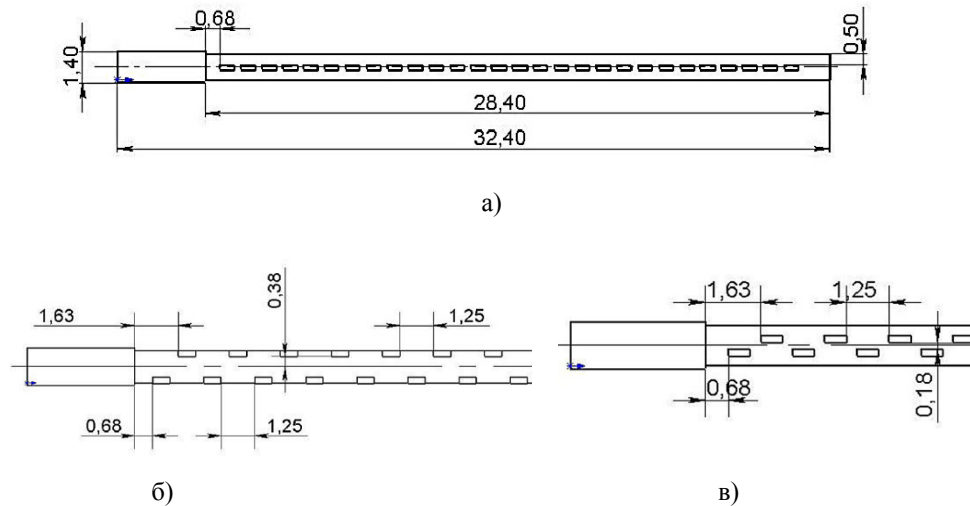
Внешний вид и габаритные размеры светодиодных излучающих элементов:
